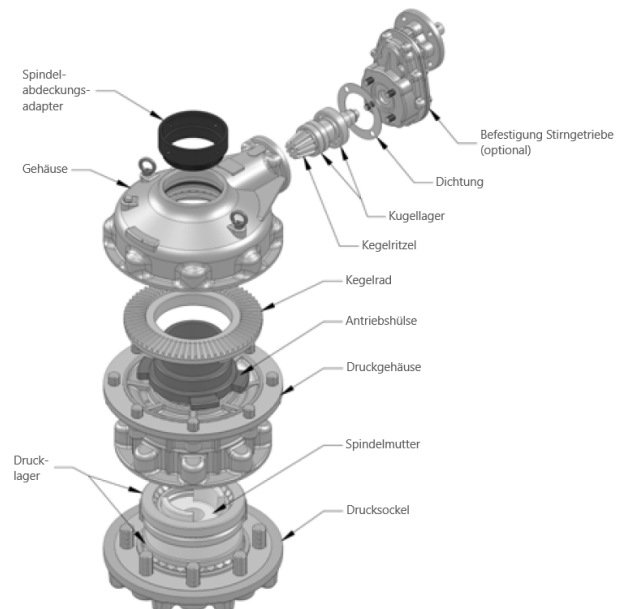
Explosionsansicht eines Standard SB VH Getriebe
